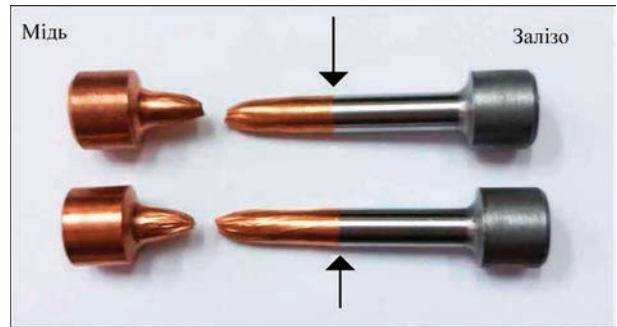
Вигляд зразків біметалічної сполуки сталь-мідь після випробування на розрив
